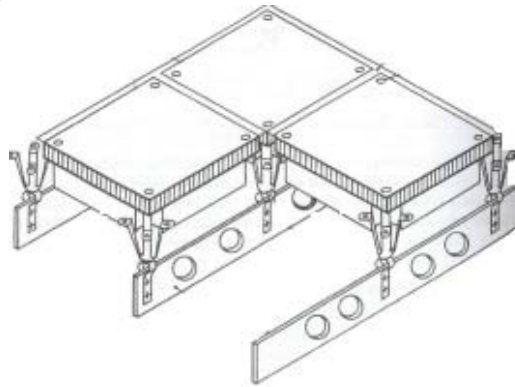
Схема конструкции металлической теплозащиты корабля «ВЕНЧУРСТАР»
